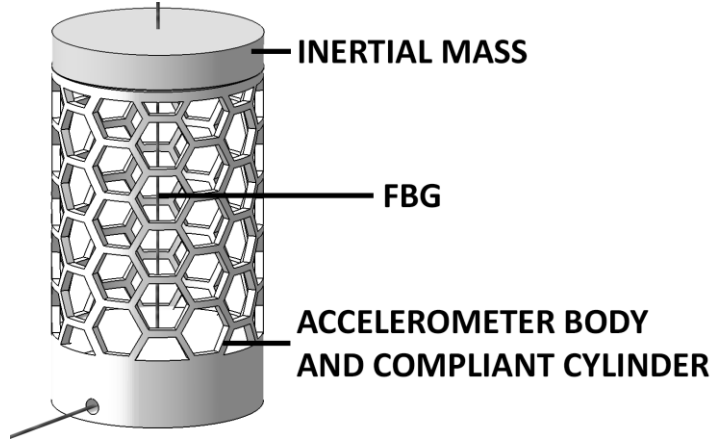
Vista CAD del sensor propuesto: Masa inercial, FBG y cuerpo del acelerómetro actuando como cilindro flexible.
